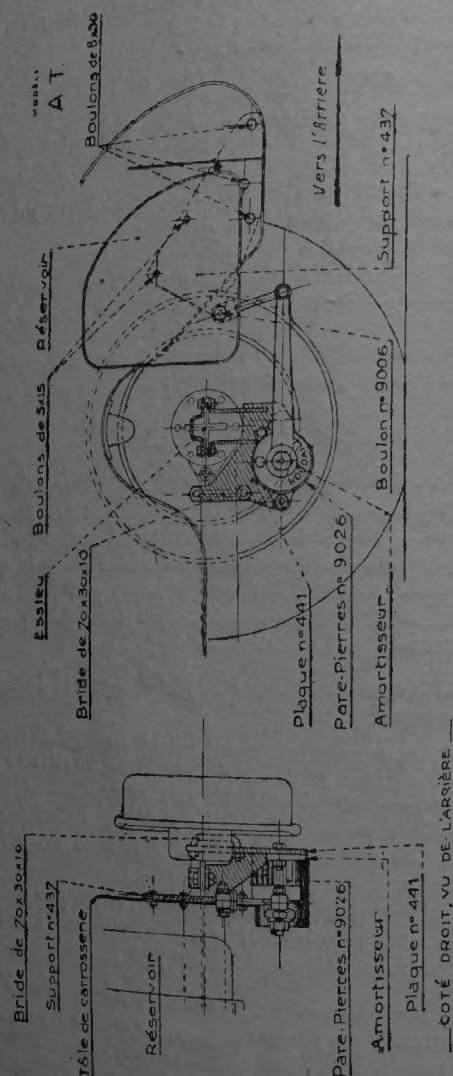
Montage d'amortisseur Houdaille sur essieu cruciforme.
